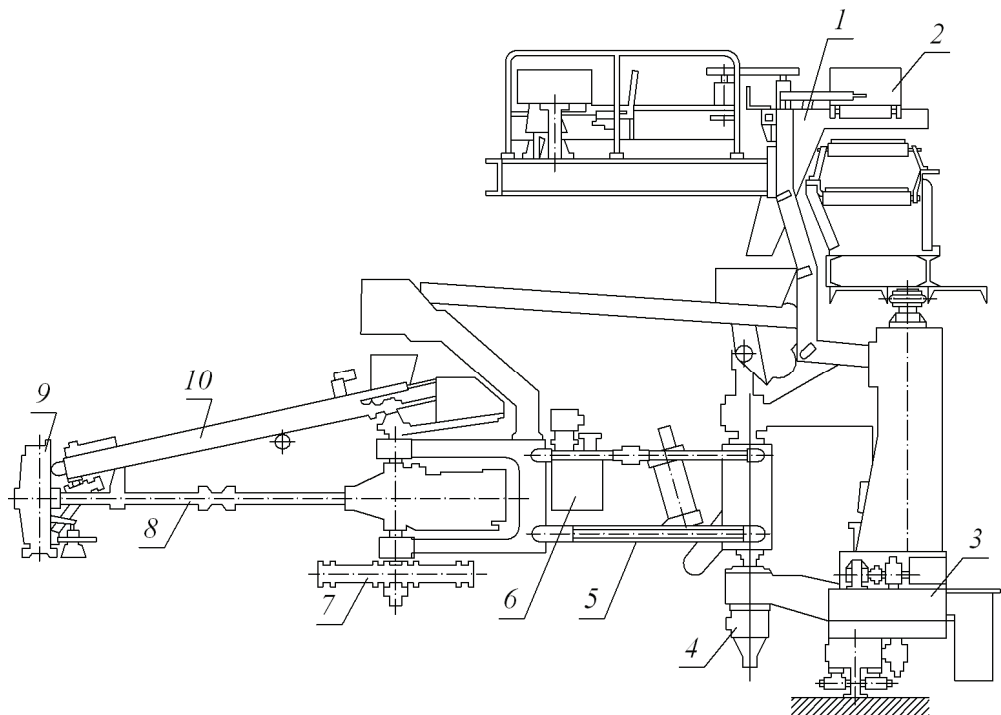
Общий вид пескомета модели 24437: 1 – механизм сброса смеси; 2 – цеховой конвейер подачи смеси; 3 – тележка; 4 – механизм поворота большого рукава; 5 – большой рукав; 6 – насосные станции; 7 – механизм поворота малого рукава; 8 – малый рукав; 9 – головка пескометная; 10 – конвейер малого рукава; 11 – конвейер большого рукава; 12 – площадка управления
